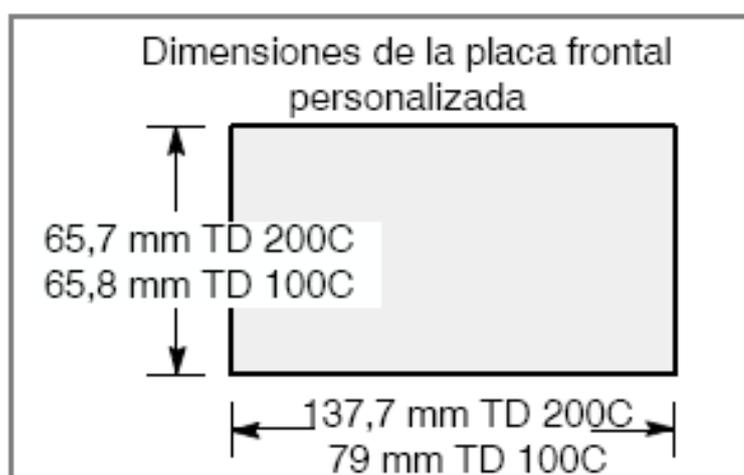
Dimensiones de la Placa Frontal Personalizada.
